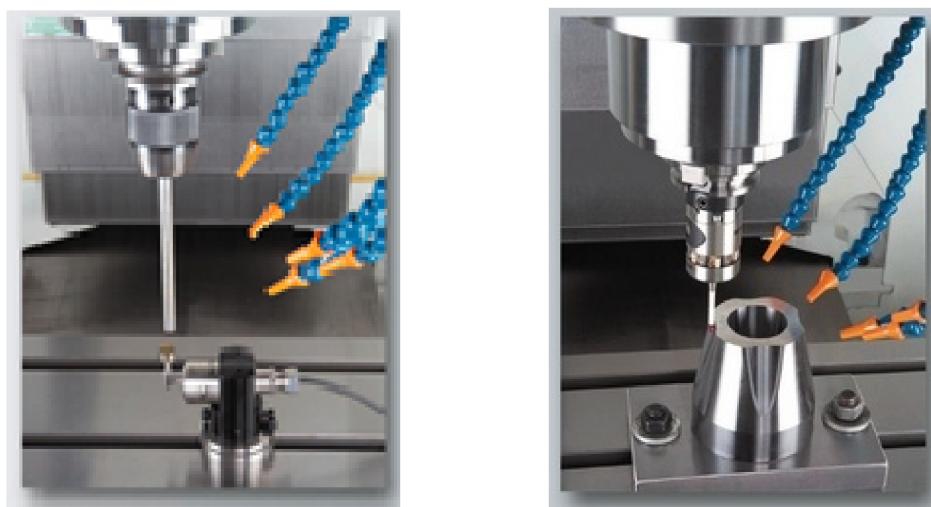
Щупи RENISAW для деталі і інструменту
